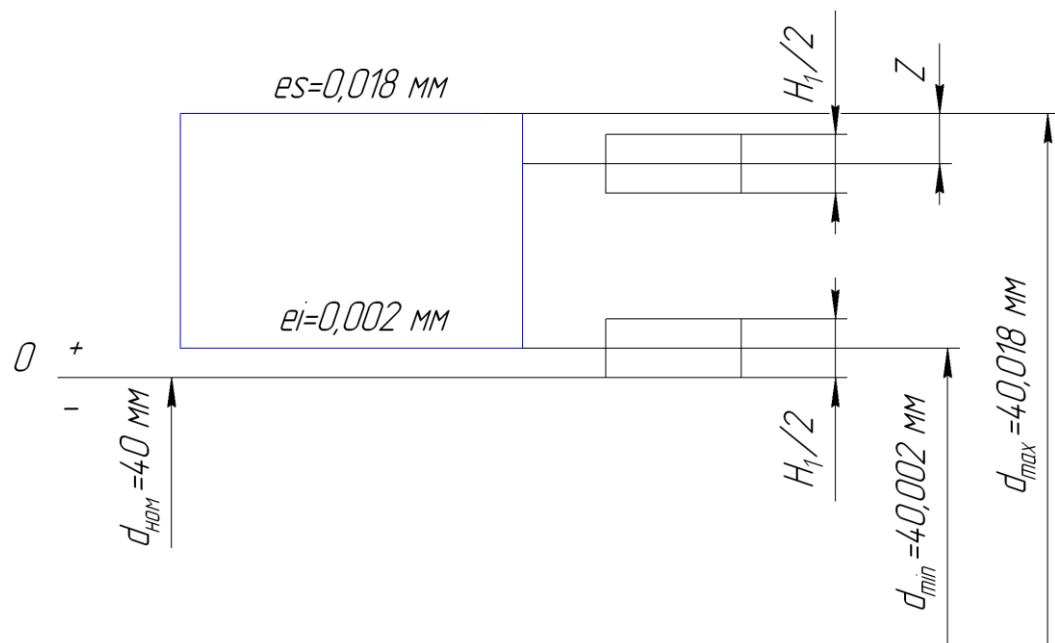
Схема розташування допусків робочих поверхонь скоби для контролю розміру $\varnothing 40k6 \begin{matrix} +0,018 \\ +0,002 \end{matrix}$
